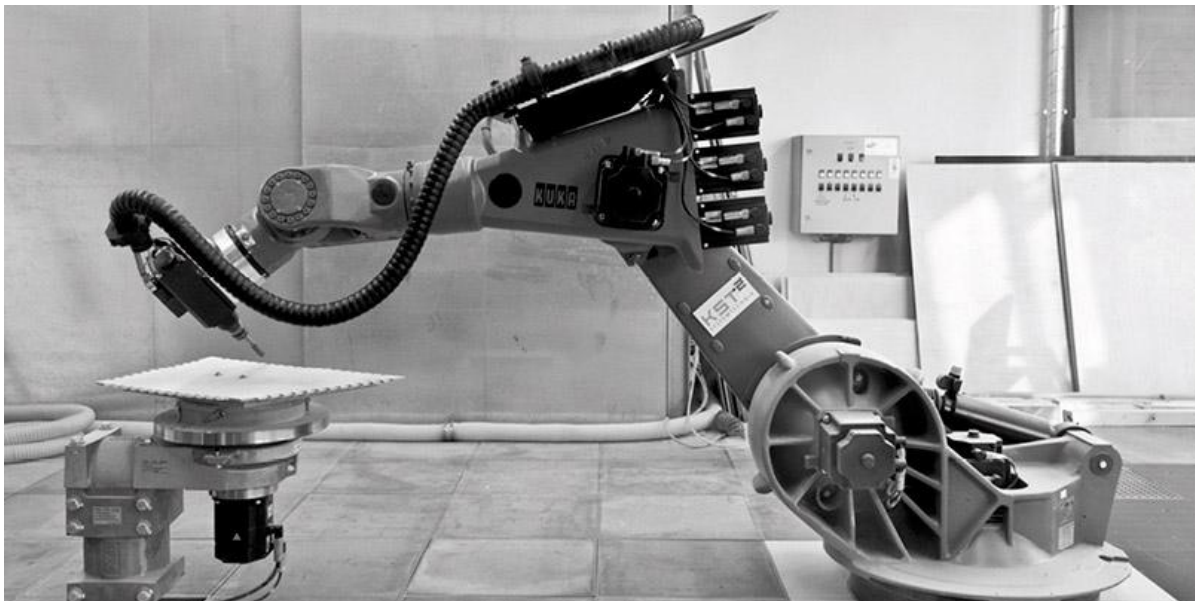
Robotische Fertigungsanlage mit sieben Achsen zum spanenden Bearbeiten von Holz und Holzwerkstoffen. Sowohl Werkzeug als auch Effektor können während der Bearbeitung gewechselt werden.
